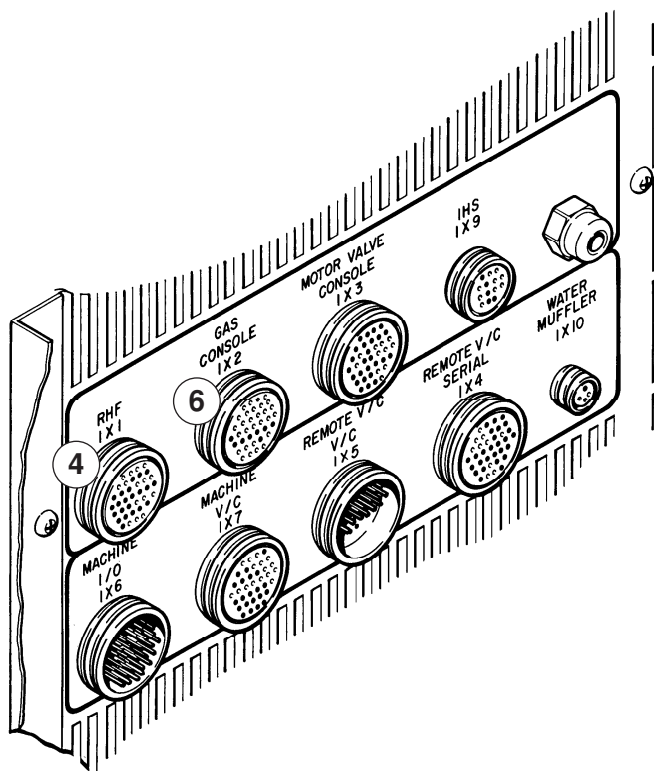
Collegamenti dall'alimentatore alla console RHF
